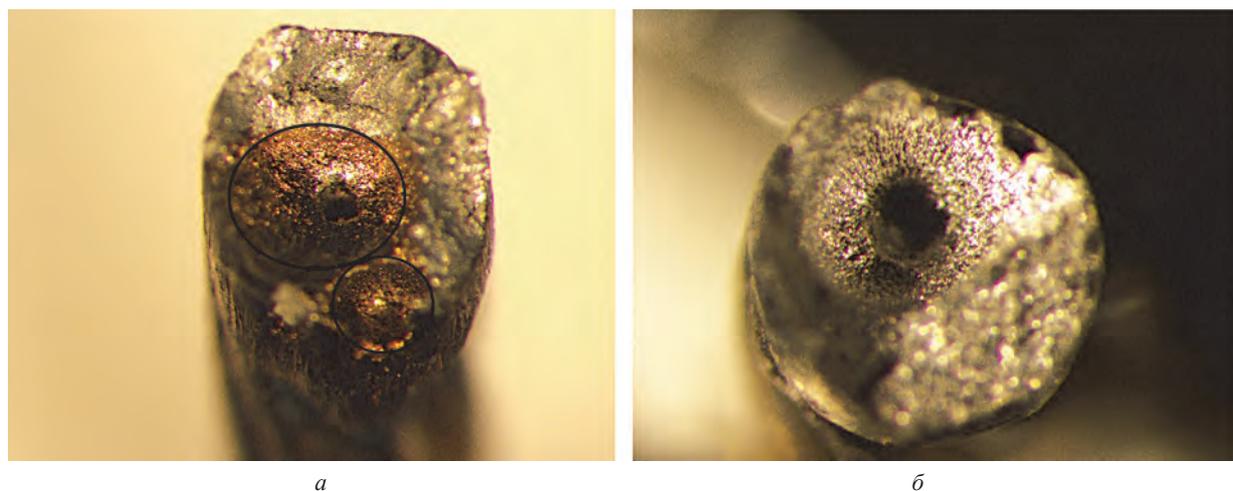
Расположение внутренних полостей в объеме сварных соединений, выявленных в обрывах сварки металлокорда: а – две окисленные полости в объеме сварки; б – одна полость без следов окисления
